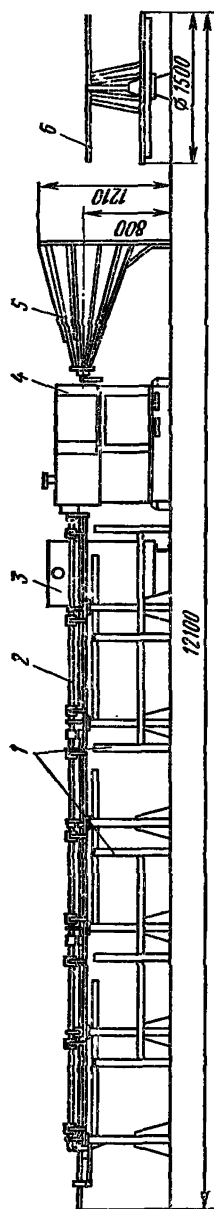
Установка СМЖ-357 для правки и резки арматурной стали:
